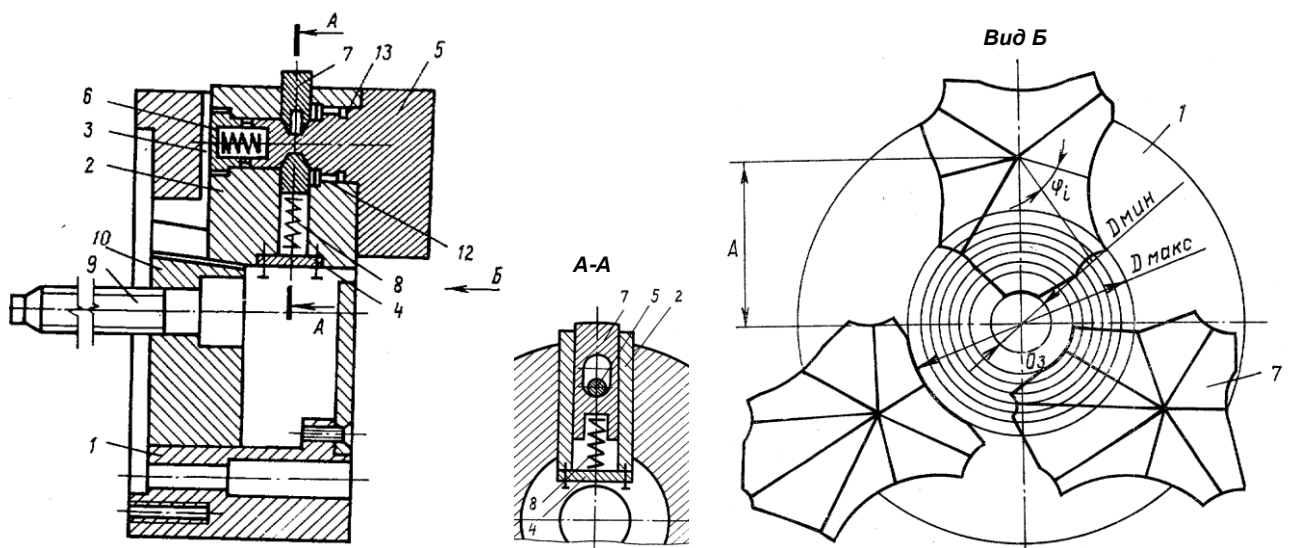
Швидкопереналагоджувальний токарний патрон із поворотними багатопрофільними затискними елементами
